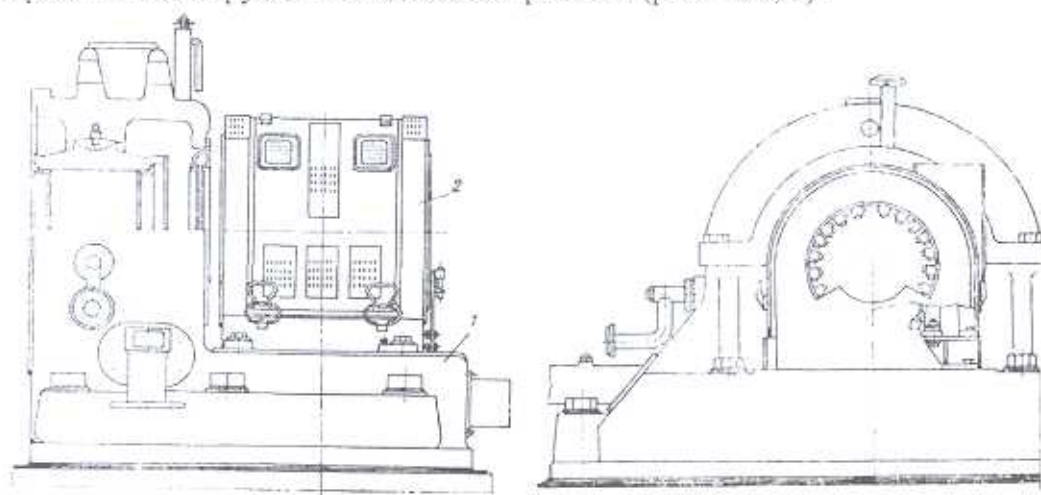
Опорный подшипник с установленным на нем щеткодержательным аппаратом:
